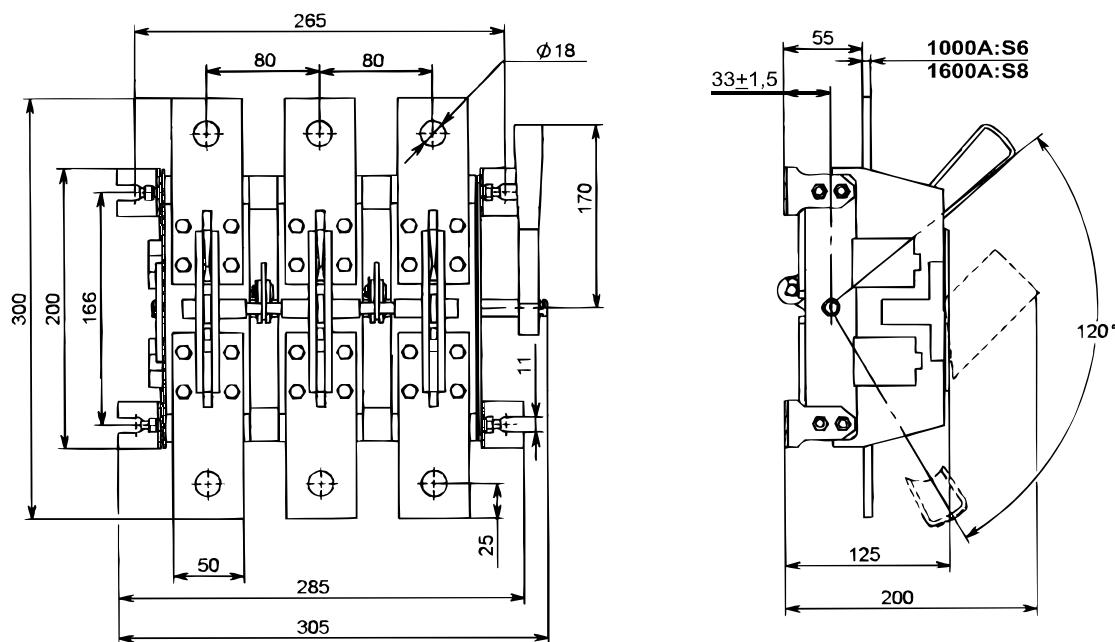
Разъединитель РЕ19-41(43)-31120-00 УХЛЗ с боковой рукояткой
